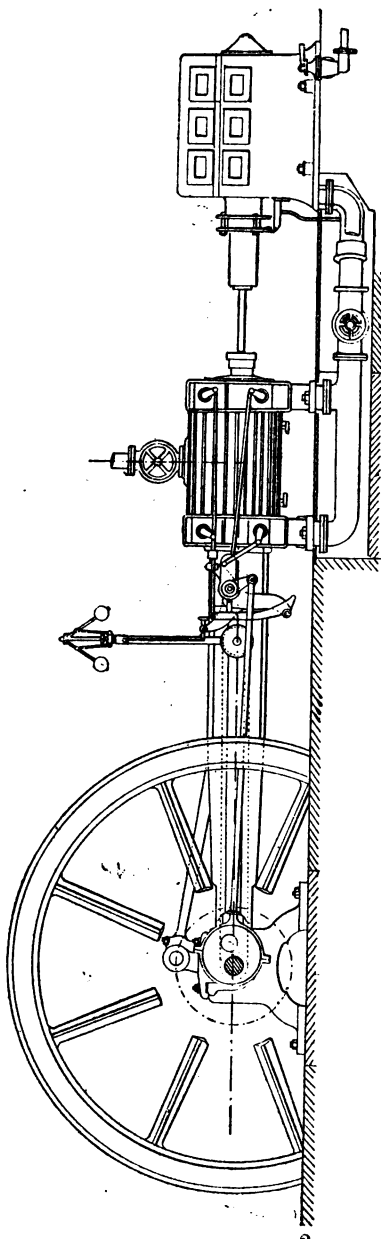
Machine horizontale à faible vitesse Lecouteux et Garnier.
